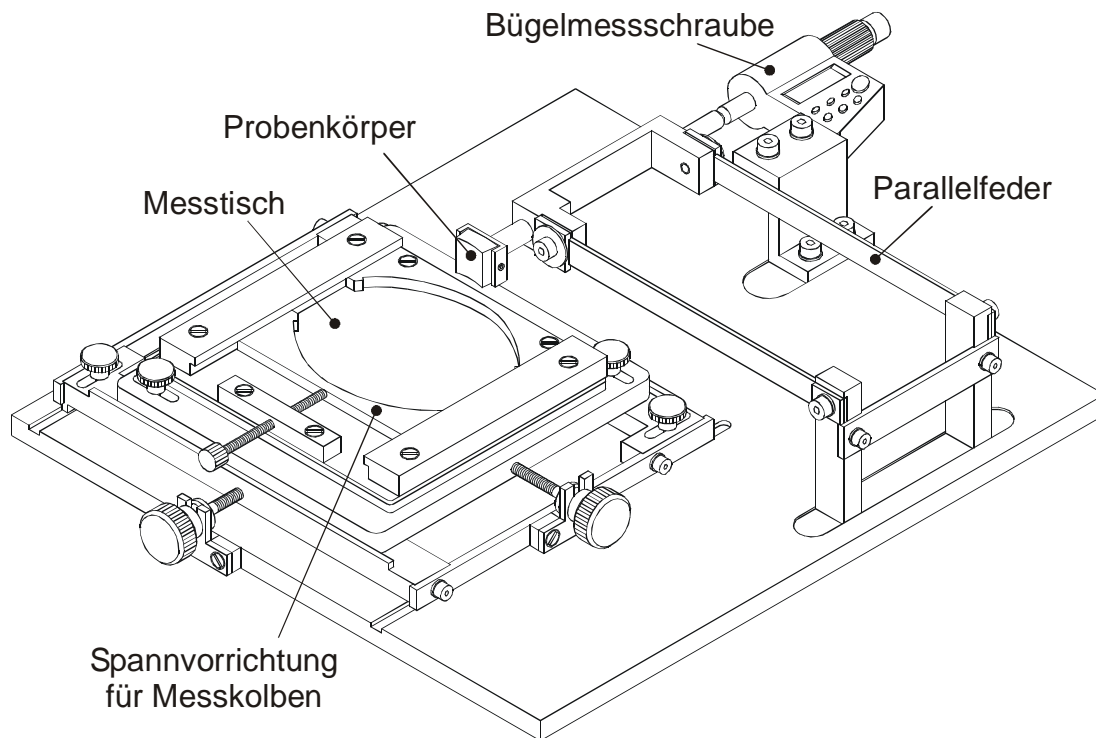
Aufbau der Kalibriereinrichtung für kompletten Messkolben
